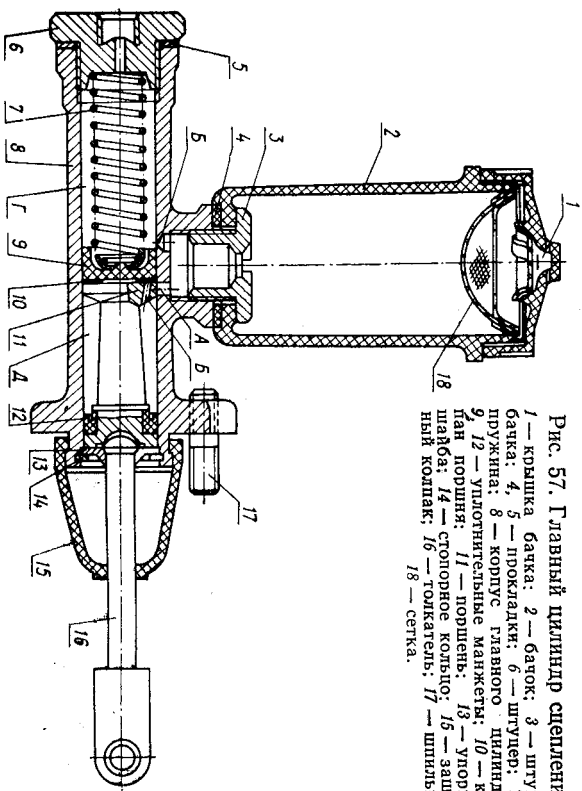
Главный цилиндр сцепления: 1 — крышка бачка; 2 — бачок; 3 — штуцер бачка; 4, 5 — прокладки; 6 — штуцер; 7 — пружина; 8 — корпус главного цилиндра; 9, 12 — уплотнительные манжеты; 10 — клапан; 11 — поршень; 13 — упорная шайба; 14 — стопорное кольцо; 15 — защитный колпак; 16 — толкатель; 17 — шпилька; 18 — сетка.
